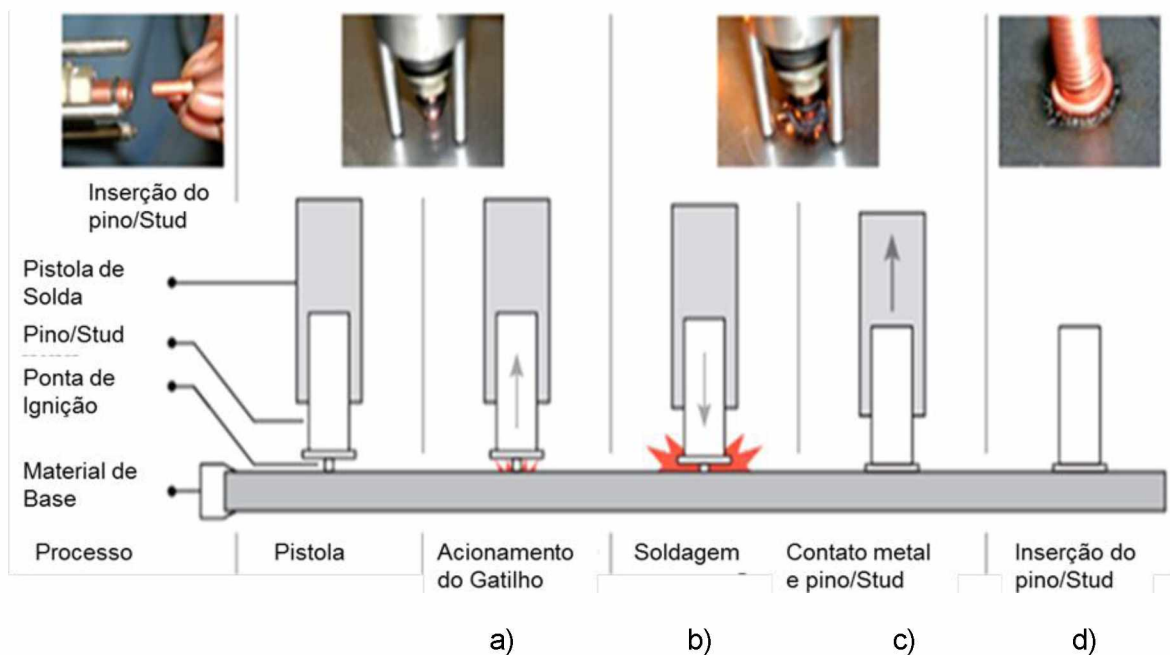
Seqüência de deposição de pinos com o Processo de Soldagem do Pino de Descarga do Condensador (RIVET & WELDSTUD MANUFACTURING CC, 2015)
